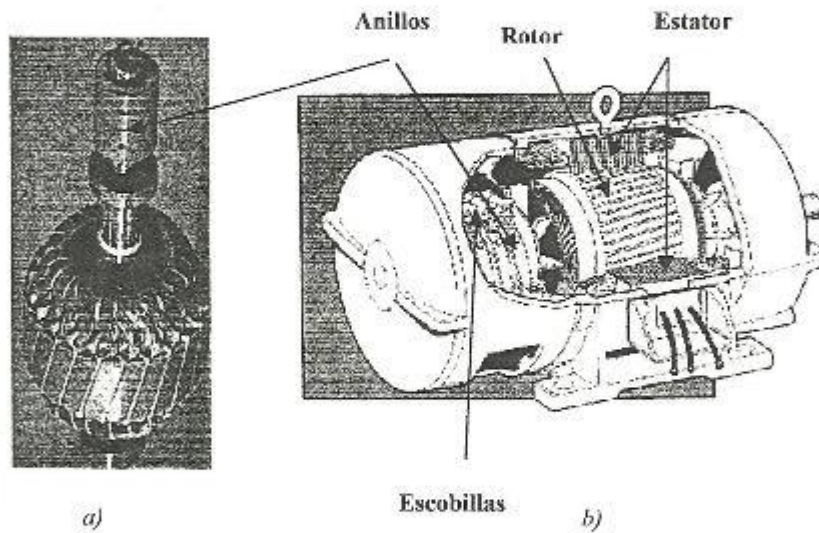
a) Fotografía de un rotor devanado. b) Dibujo del corte de un motor de inducción de rotor devanado indicando sus partes
